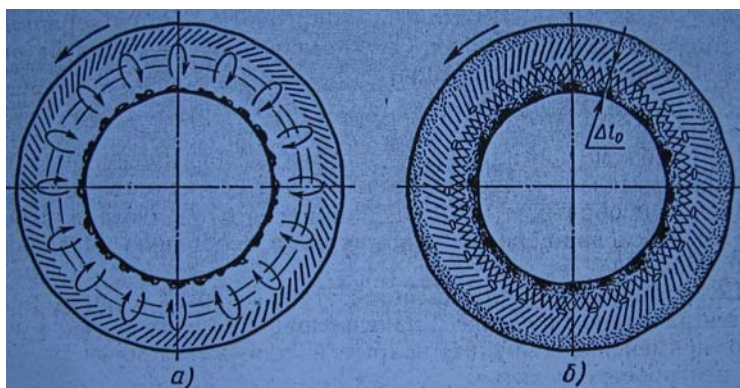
Схема возникновения конвективных потоков во вращающемся и затвердевающем расплаве (а) и кристаллического строения отливки (б).
